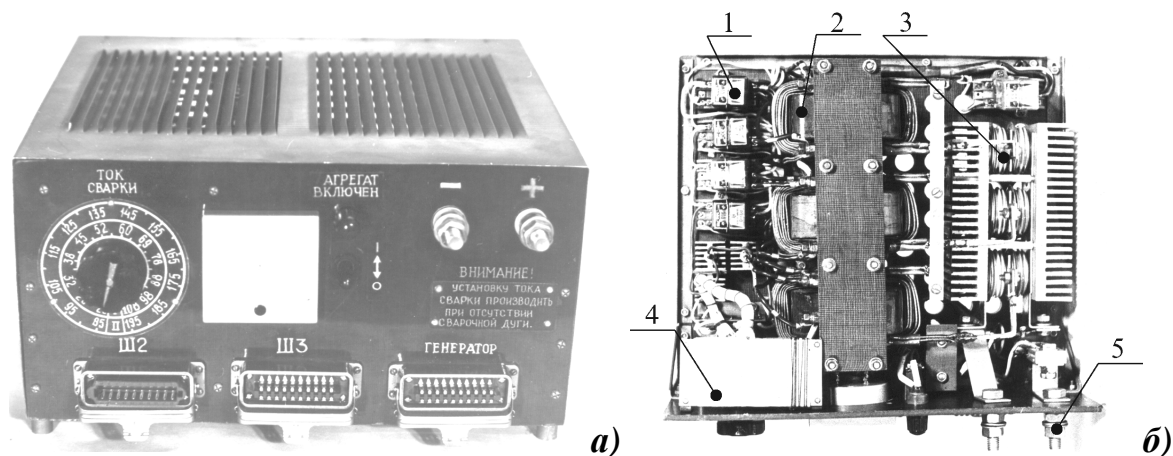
Внешний вид сварочного блока *а*), блок управления без кожуха *б*), 1 – реле; 2 – согласующие трансформаторы; 3 – силовой выпрямитель; 4 – дешифратор; 5 – выводы для подключения сварочных проводов
